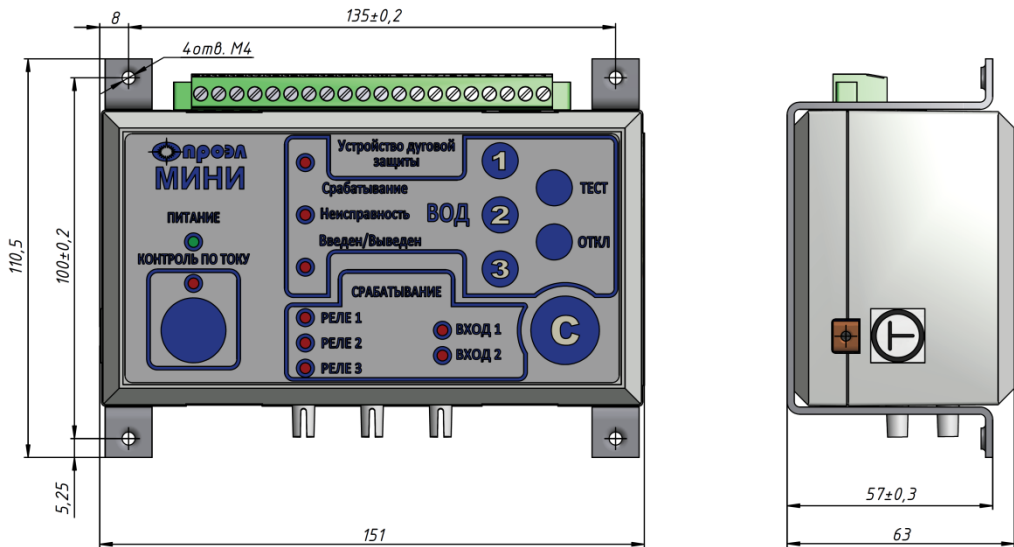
Вид и габаритные размеры БПМ в варианте крепления 02
